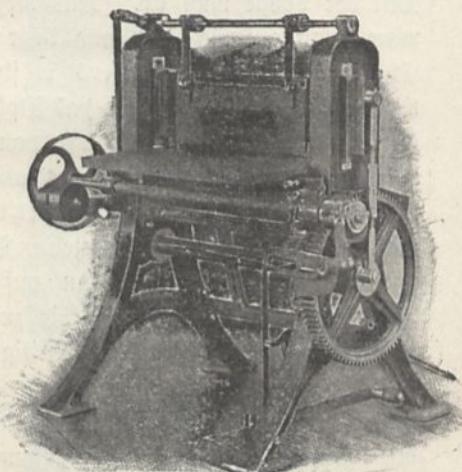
Formiermaschine für Geschäftsbücher von Karl Krause, Leipzig.
